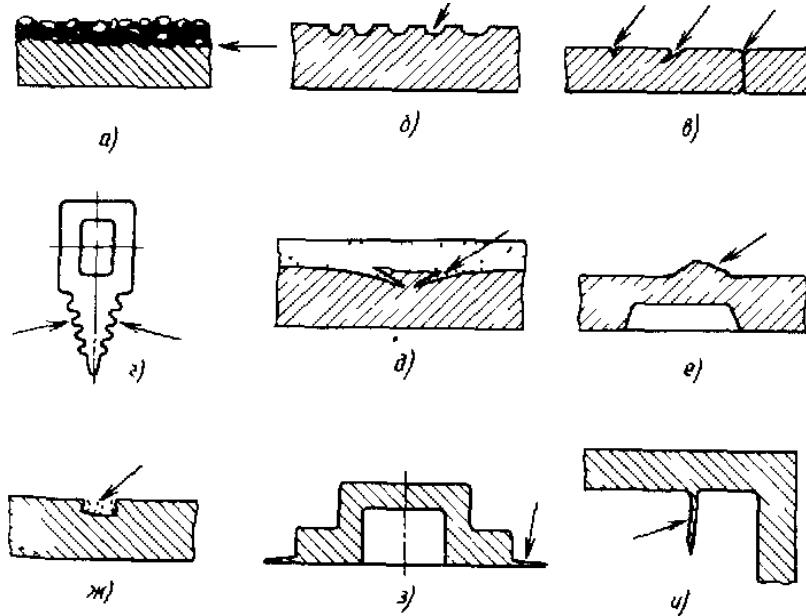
Дефекты поверхности отливки (стрелки указывают на расположение дефекта)
